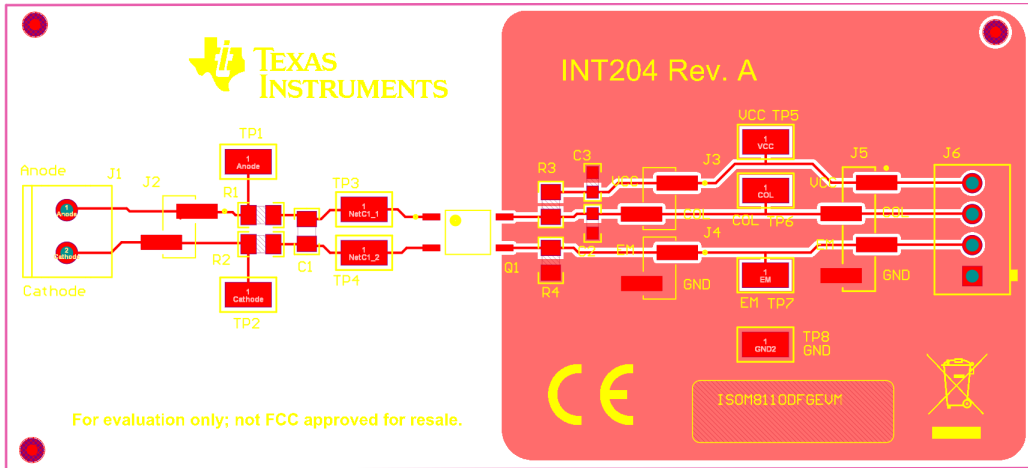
ISOM8110DFGEVM PCB 布局 - 顶层
